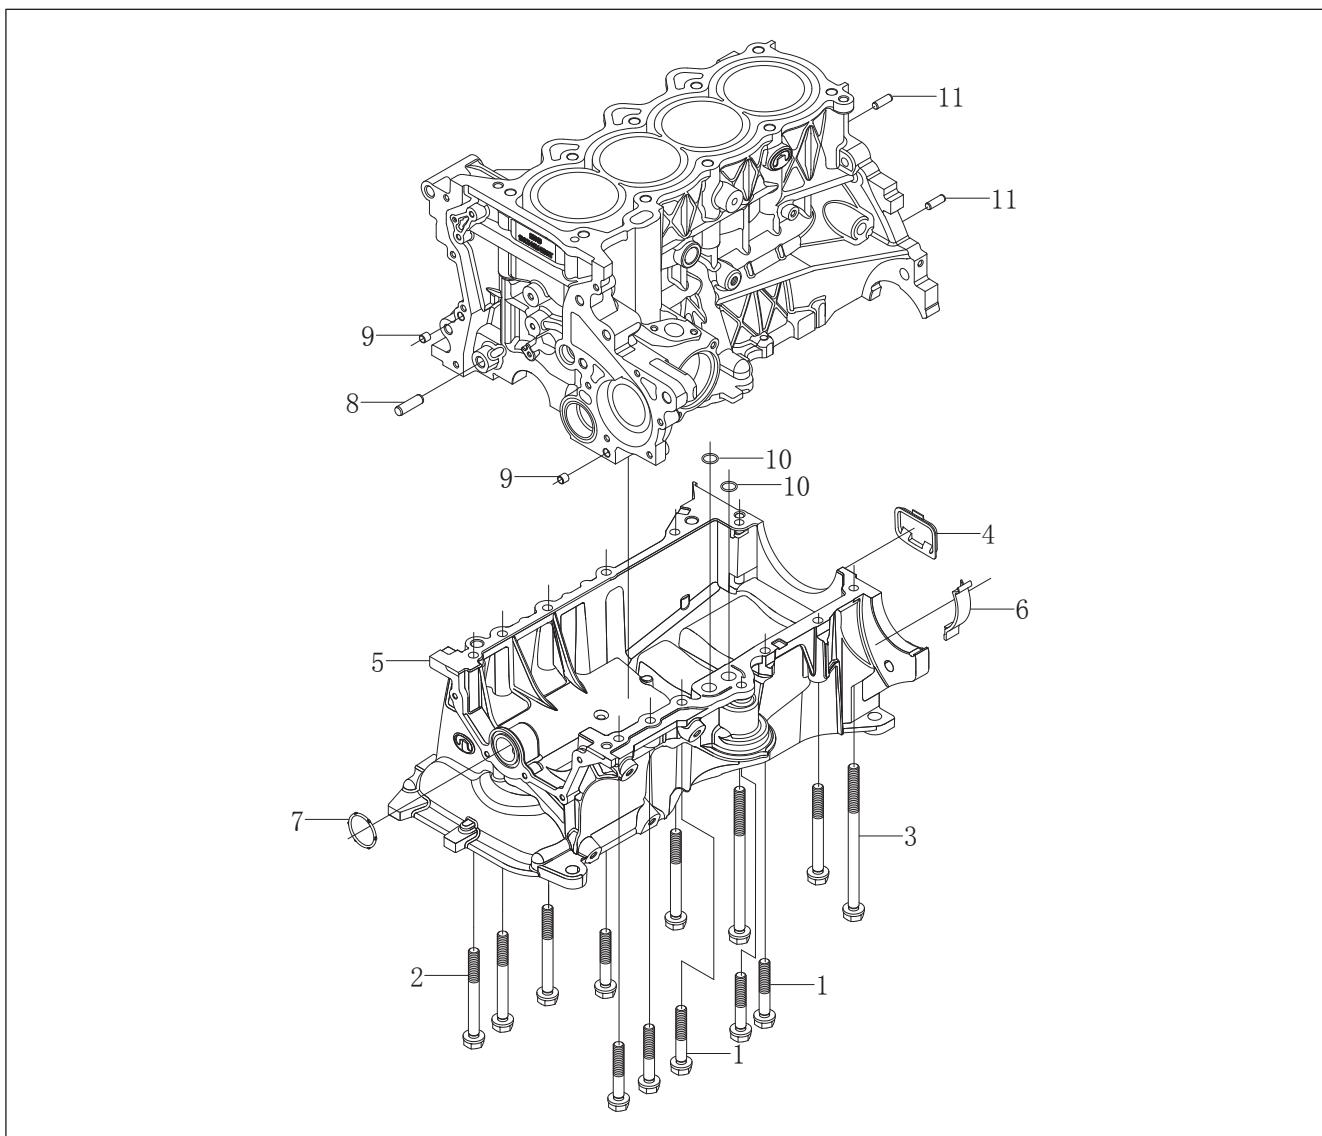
Схема расположения компонентов верхней и нижней частей блока цилиндров бензинового двигателя
